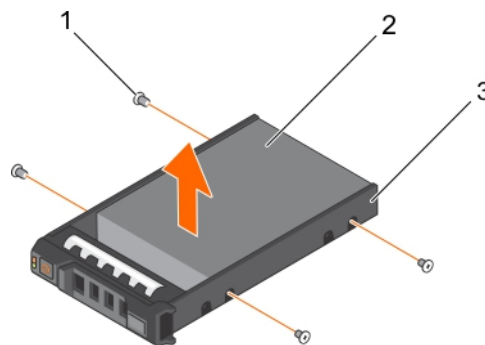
Retrait d'un disque dur remplaçable à chaud installé dans un support de disque dur
